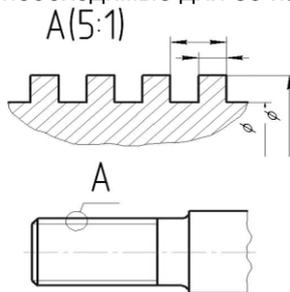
Изображение и обозначение нестандартной прямоугольной резьбы
